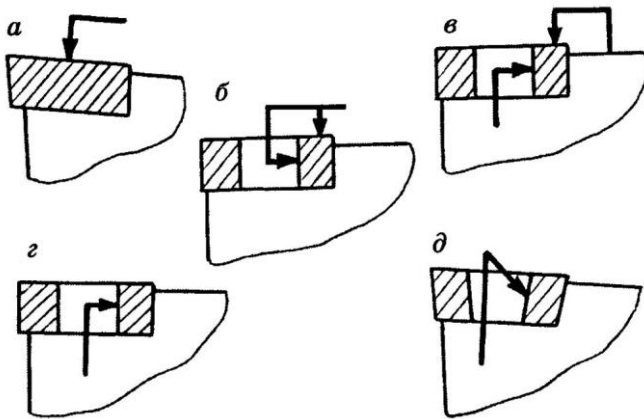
Схемы крепления СМП в корпусах инструментов
